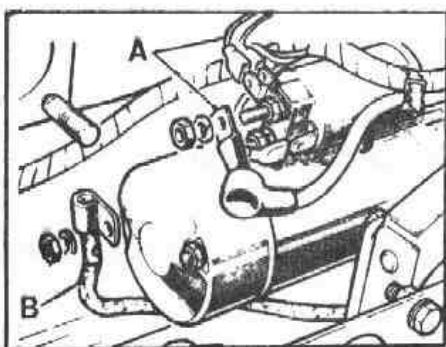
Desmontaje de cables de alimentación del motor y cable de masa
